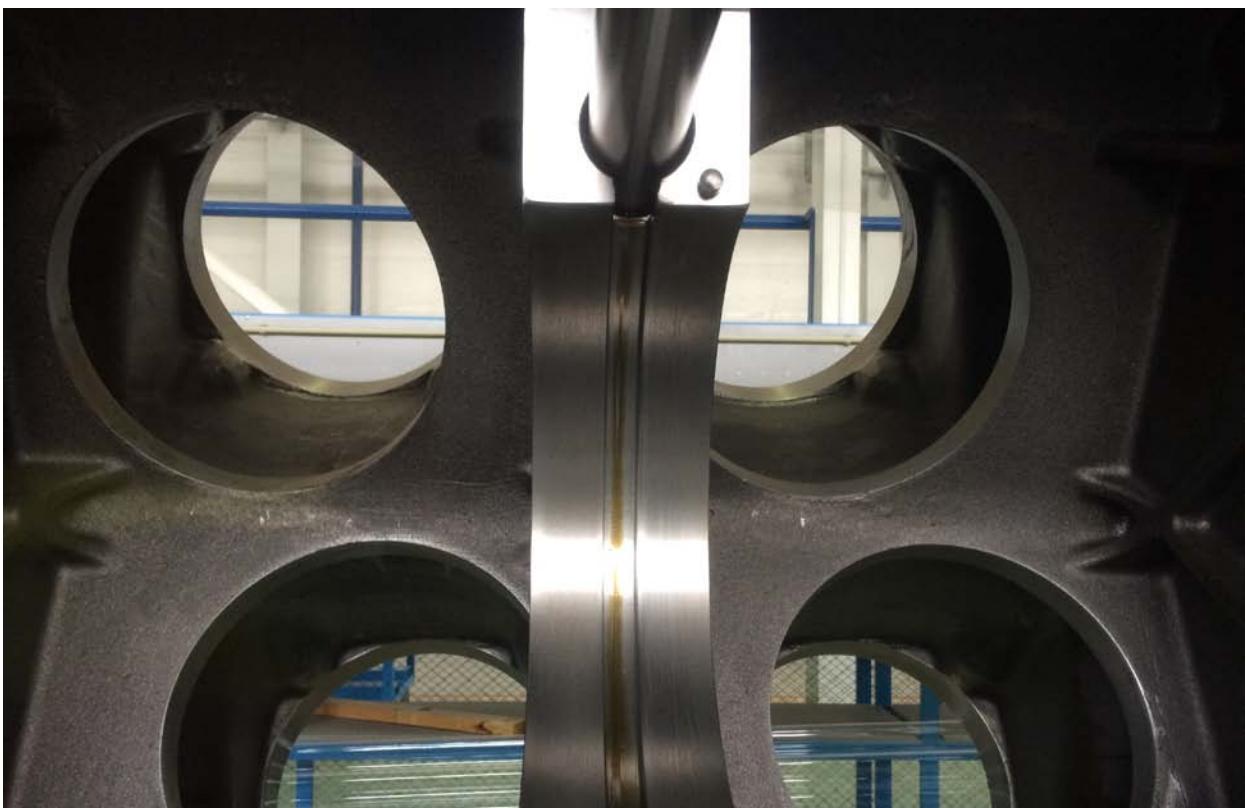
Рама двигателя - вид снизу. В коренной подшипник вкручены шпильки.
